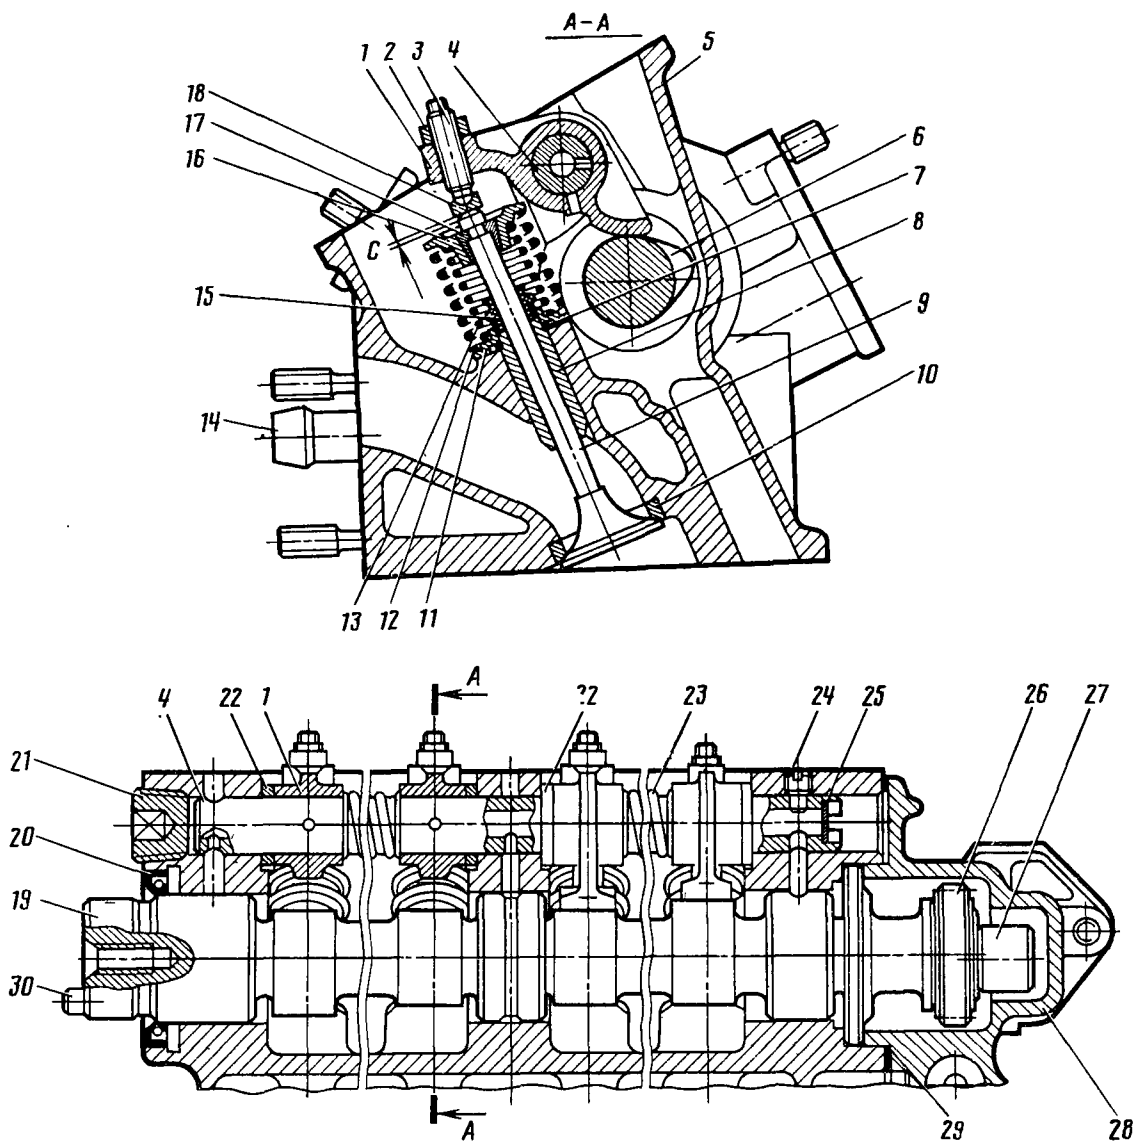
Головка цилиндров и схема регулировки зазоров в механизме привода клапана:
